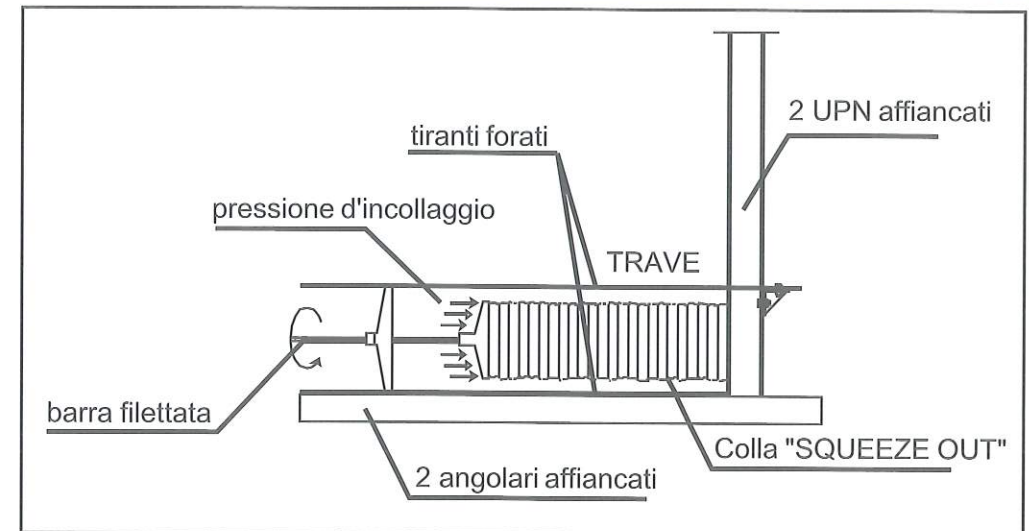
Zona di assemblaggio della trave e schema di funzionamento del letto di pressaggio
